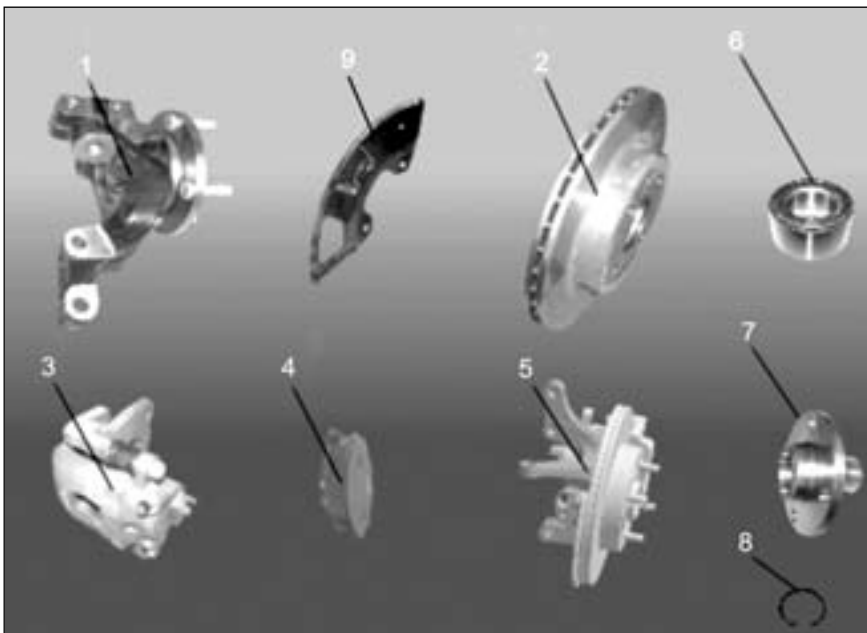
Передний поворотный кулак с тормозными дисками:
